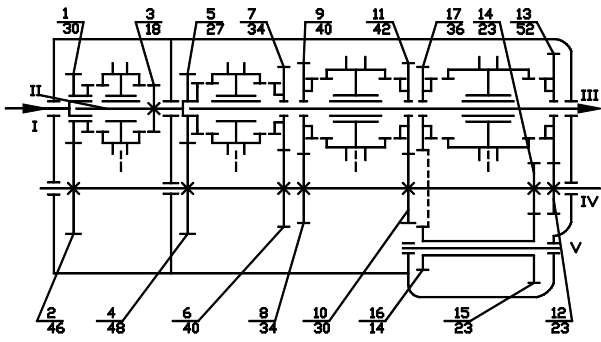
Коробка передач с редуктором-делителем (10-ступенчатая)
